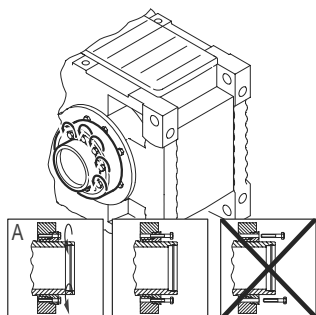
Vis d'assemblage de la frette de serrage avant le montage de l'arbre client
